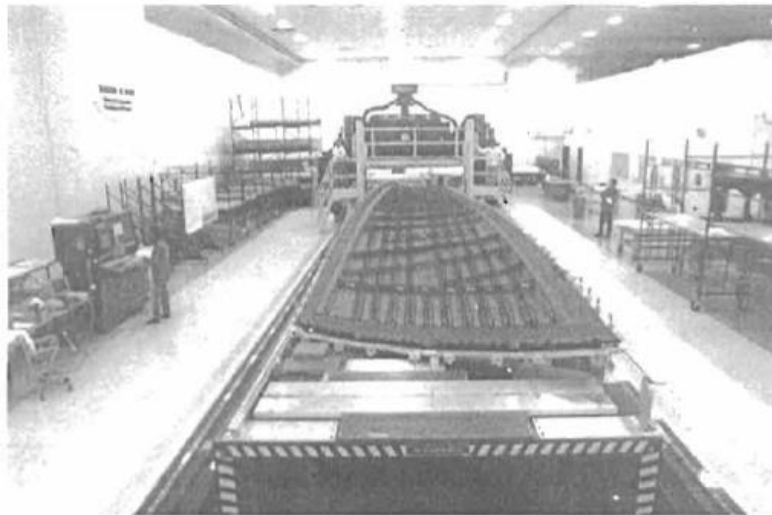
Máquina de coser utilizada para coser alas de materiales compuestos [22]
